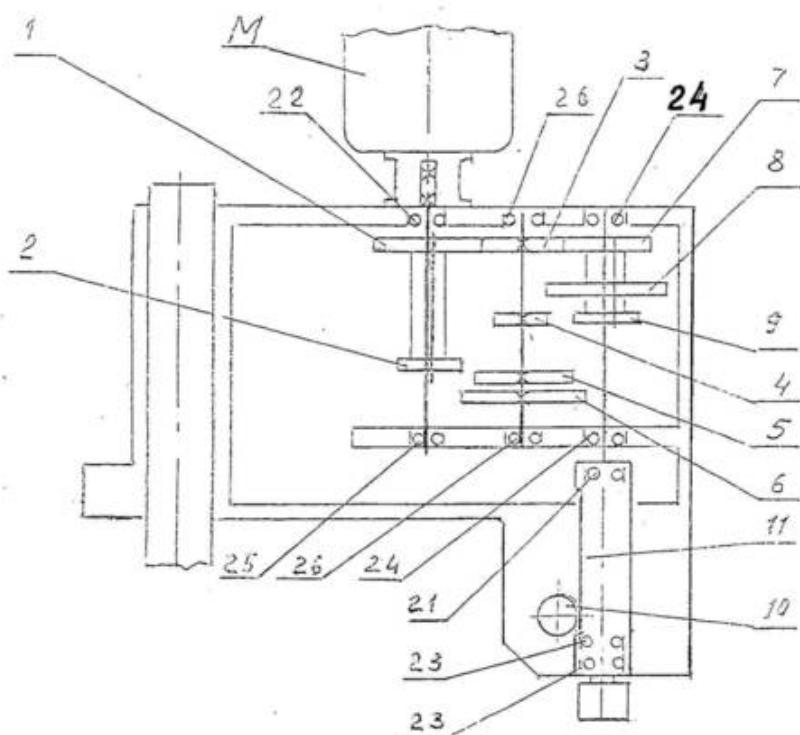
Кинематическая схема сверлильной головки и схема расположения подшипников
